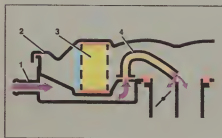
Удлинитель вентиляционной трубки позволяет избежать застигивания бумажного фильтра: 1 — корпус; 2 — крышка; 3 — фильтр; 4 — удлинитель.
